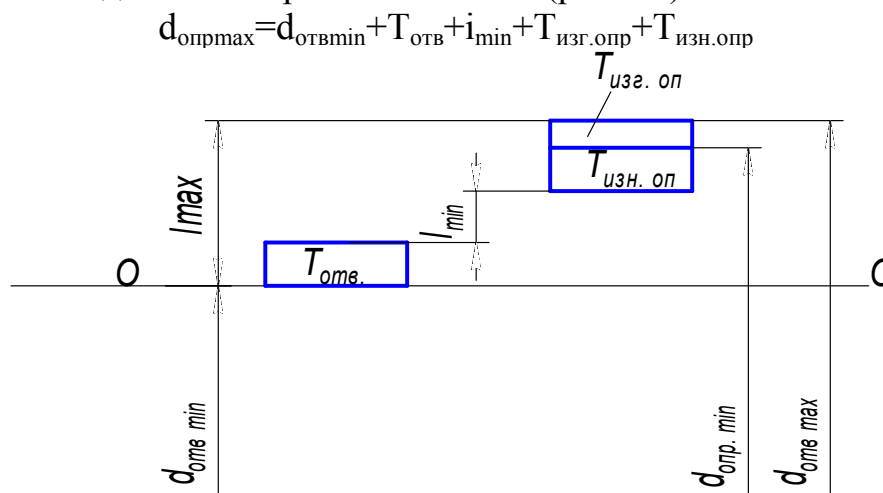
Схема расположения полей допусков соединения оправка-заготовка
